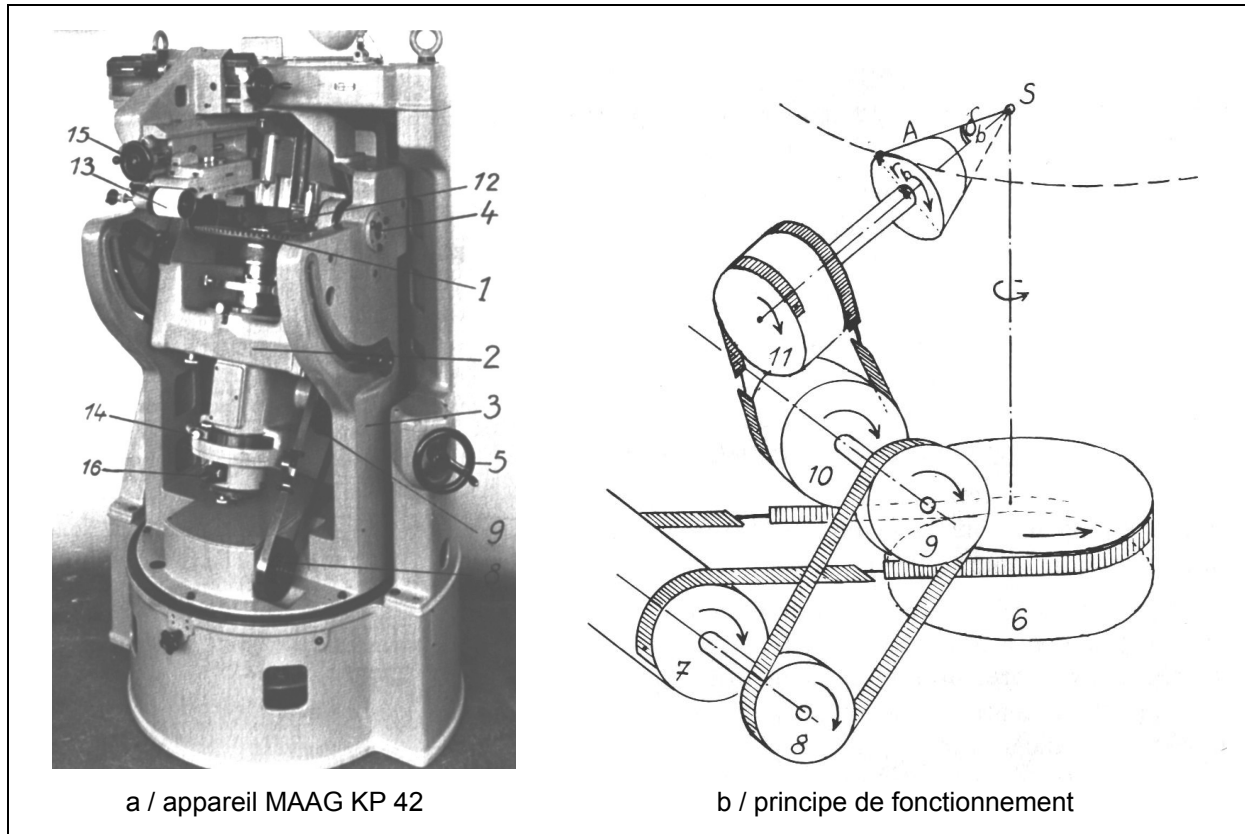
Machine à contrôler les engrenages MAAG KP 42 [HEN83].
